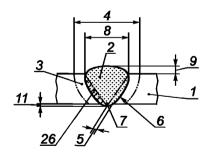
Configuration pour soudure à la molette avec feuillard d'apport
